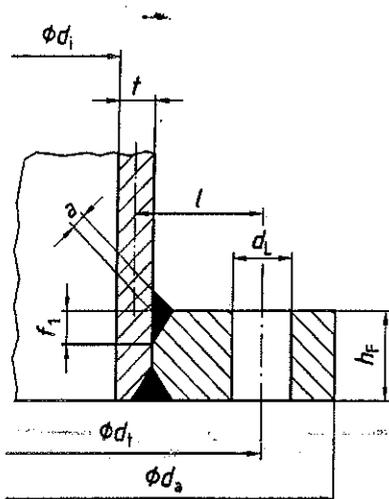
Aufschweißflansch (ohne Dichtung dargestellt)
